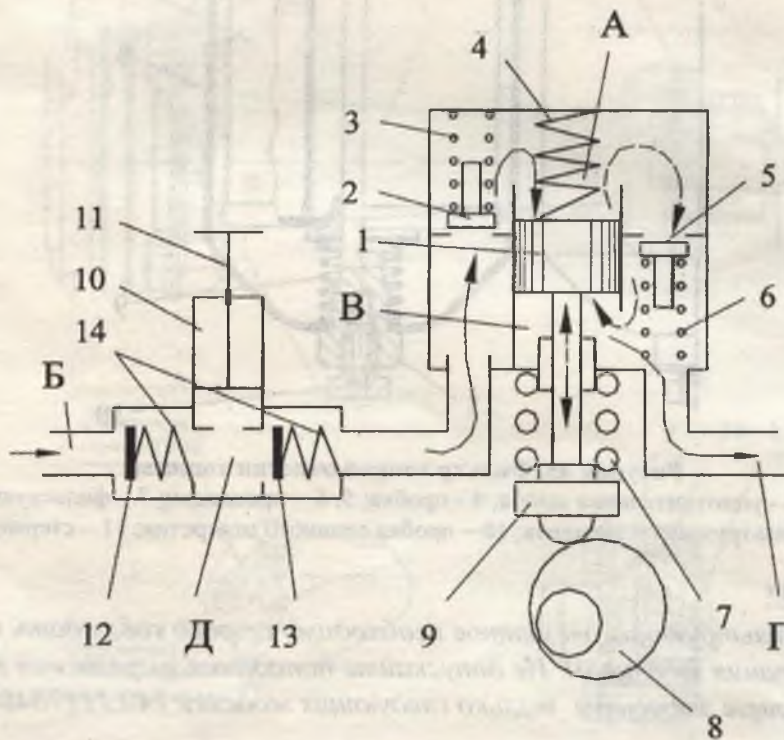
Схема работы топливоподкачивающего и топливопрокачивающего насосов:
